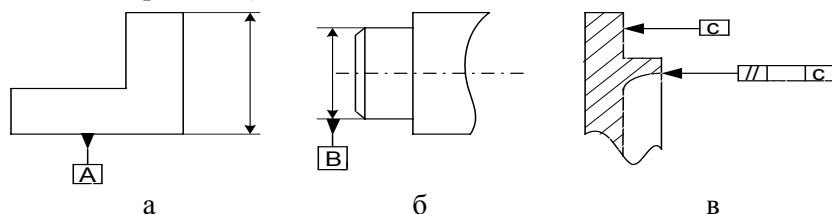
Правила нанесения на чертежах деталей условных обозначений баз:
